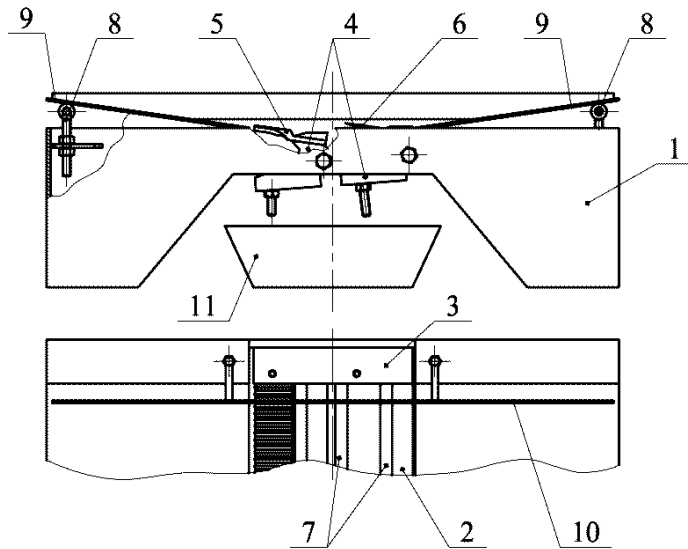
Схема модуля експериментальної установки для нарізання бурякової стружки: 1 – корпус; 2 – двохрядна ножова рама; 3 – корпус ножової рами; 4 – поворотні стійки; 5 – перший ряд ножів; 6 – другий ряд ножів; 7 – прижимні планки; 8 – пристрій для регулювання кута нахилу робочого столу; 9 – робочий стіл; 10 – напрямна пластина; 11 – лоток для стружки.
